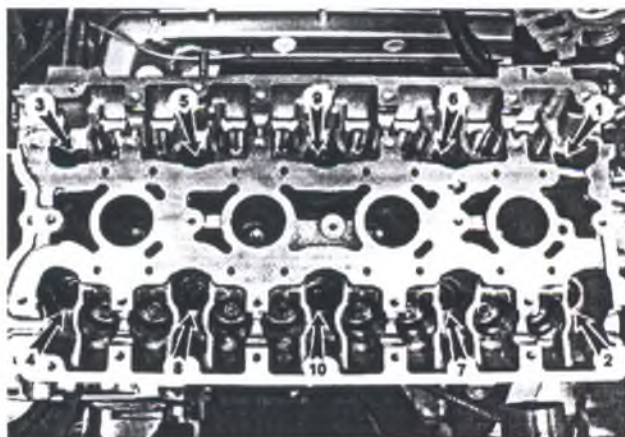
Отвинчивание болтов крепления головки блока цилиндра
